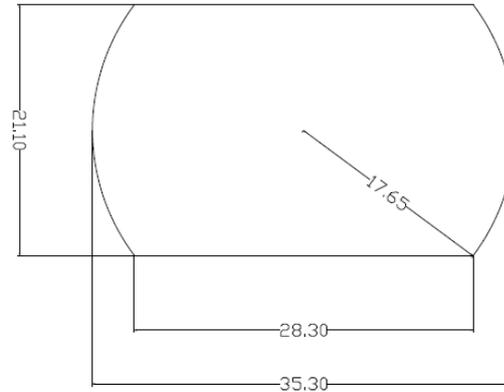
Dimensões do cabeçote Tipo 2 (em mm)
